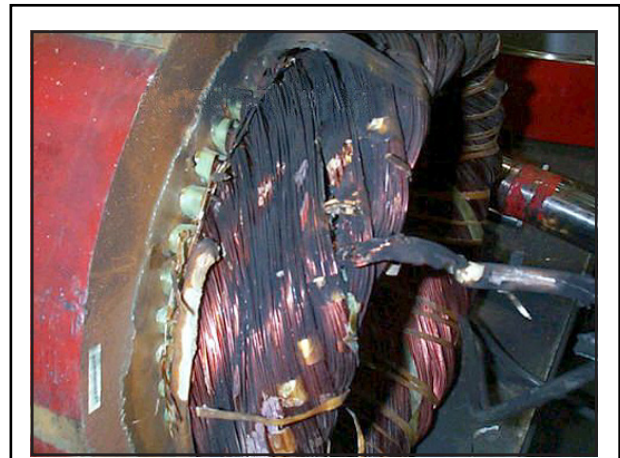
“Bobinado excéntrico o imbricado con “Bobinas enterradas”.
